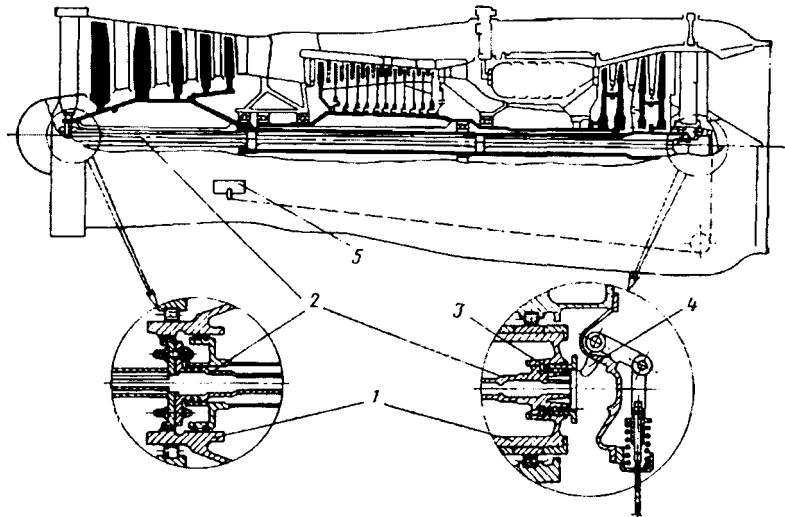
Схема механизма отсечки топлива при поломке вала ротора низкого давления ТРДД
